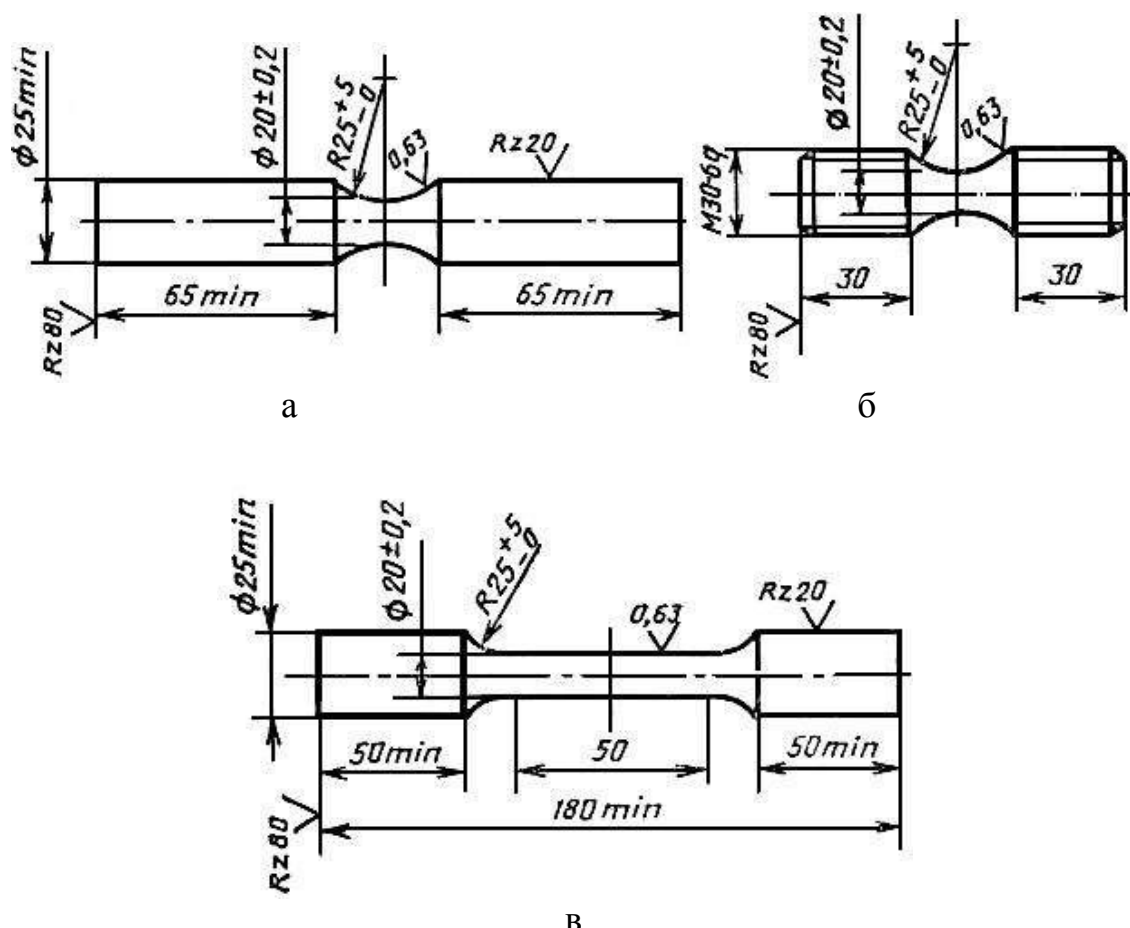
Формы и размеры образцов для испытаний на растяжение
